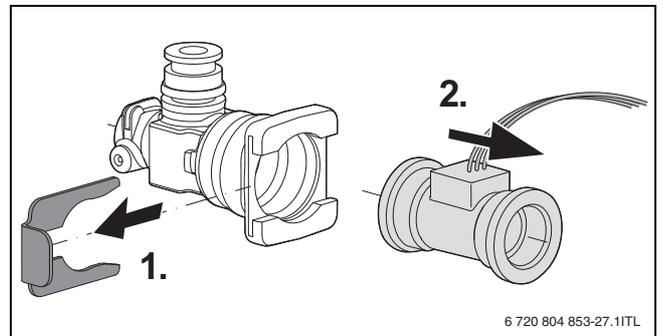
Démontez la turbine sur le tuyau d'eau froide
